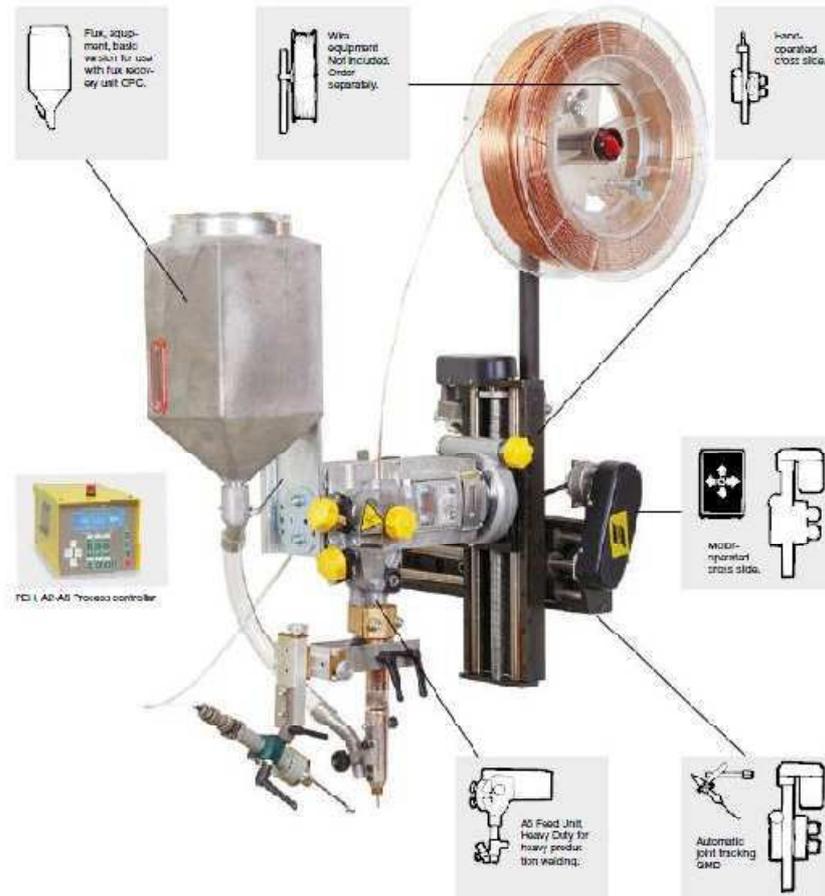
16 Cabecsal de Soldadura Motorizado A6
